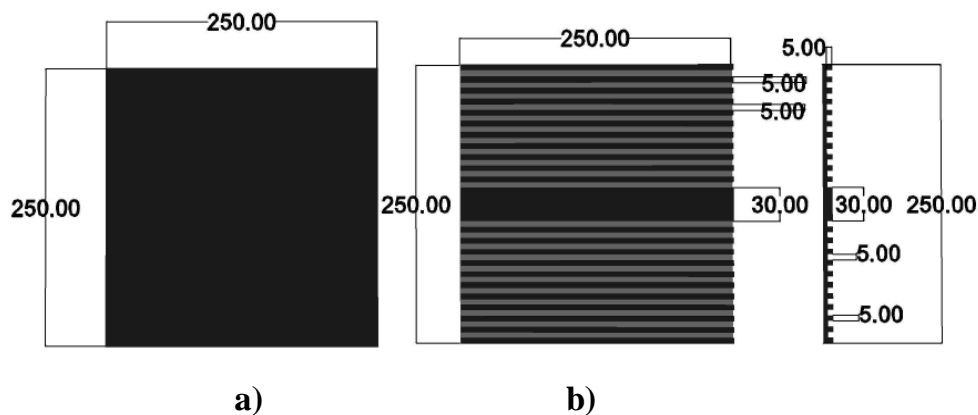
a) plaque pleine et lisse, b) plaque pleine et corruguée, (côtés en mm)
